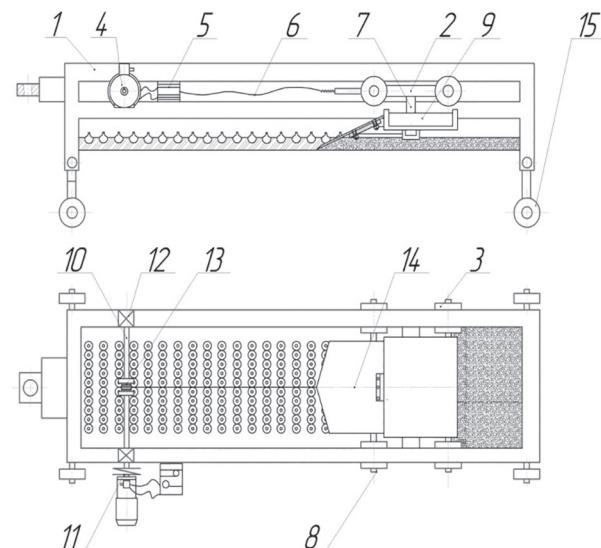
Схема лабораторной установки по определению подачи вороха лука-севка на выкапывающий лемех для уборки корнеплодов и лука:
